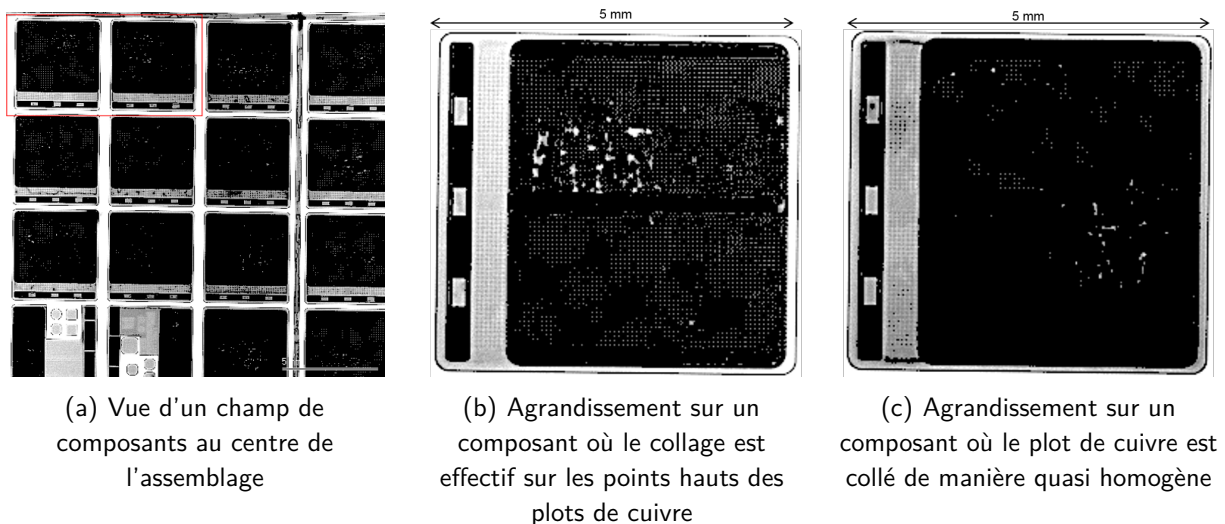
Caractérisation par microscopie acoustique du collage Cu-Cu à température d'assemblage de 350 °C de l'interface A, assemblage d'une plaque de nMOS, une plaque de cuivre polie double face et une plaque de diode; noir = zones collées et blanc = défauts ou absence de collage à cause de la topographie du composant
